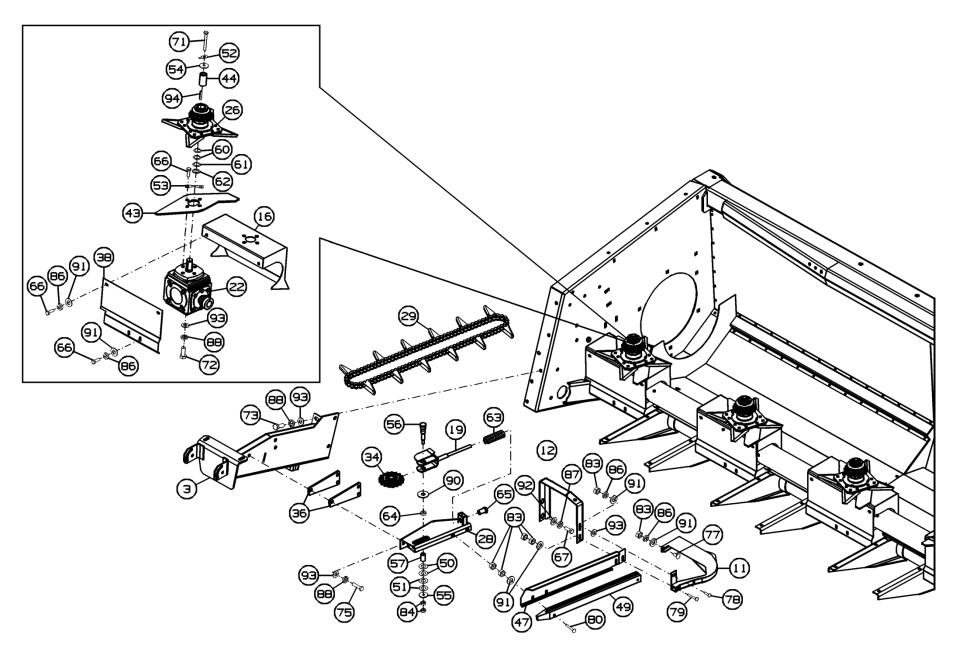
Корпус жатки ПСП-620.01.01.000
